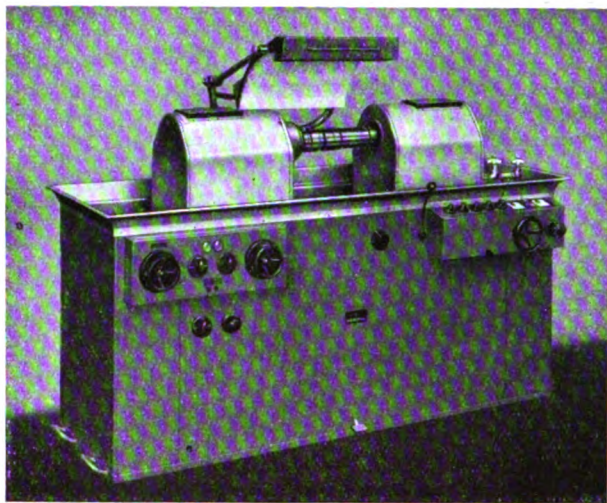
Risseprüfer für Längs- und Quermagnetisierung mit motorisch verschiebbaren Magnetschenkeln und motorisch drehbaren Einspannbacken (die Supporte sind abgenommen).
